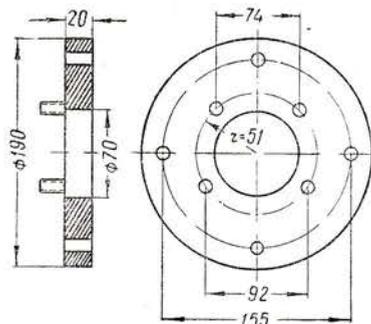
Кольцевая площадка крепления блока-цилиндра Л-3/2 (деталь приспособления для расточки и шлифовки цилиндра)
